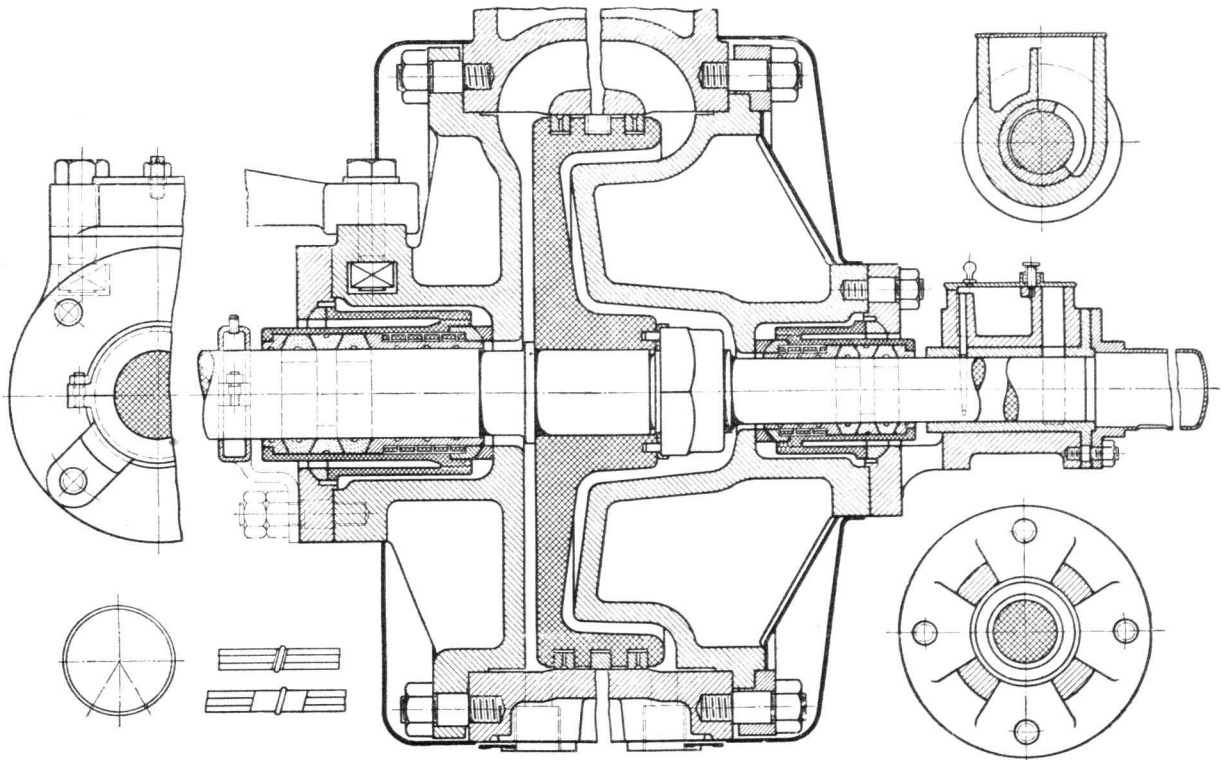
Dampfkolben mit Zylinderdeckeln und Stopfbüchsen.
